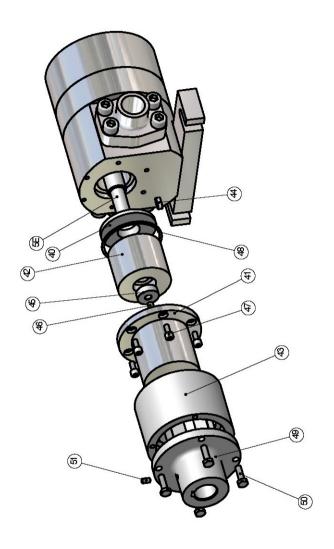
Giunto a Trascinamento Magnetico Figure 4 - Magnetic Drive Coupling
